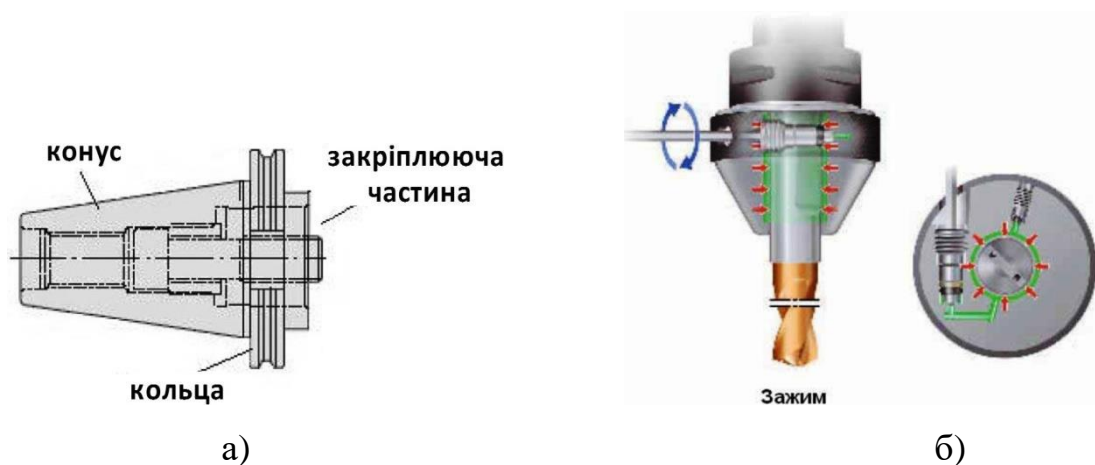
Фрезерна оправка (а) та оправка з гідропластом (б)
